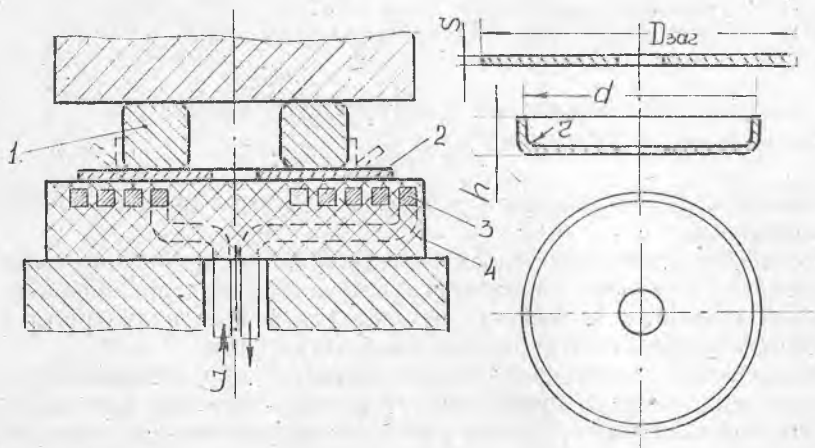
Схема процесса отбортовки наружного контура с использованием энергии ИМП: 1—матрица, 2—заготовка, 3—спираль индуктора, 4—корпус индуктора
